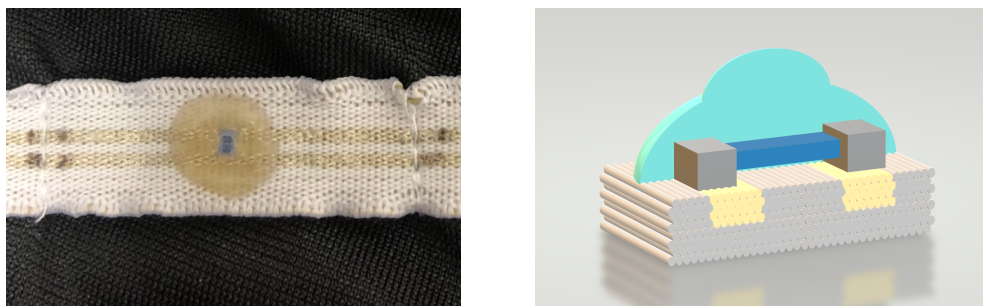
Kontaktování nevodivým lepidlem - Odebrání závaží, vznik díry
